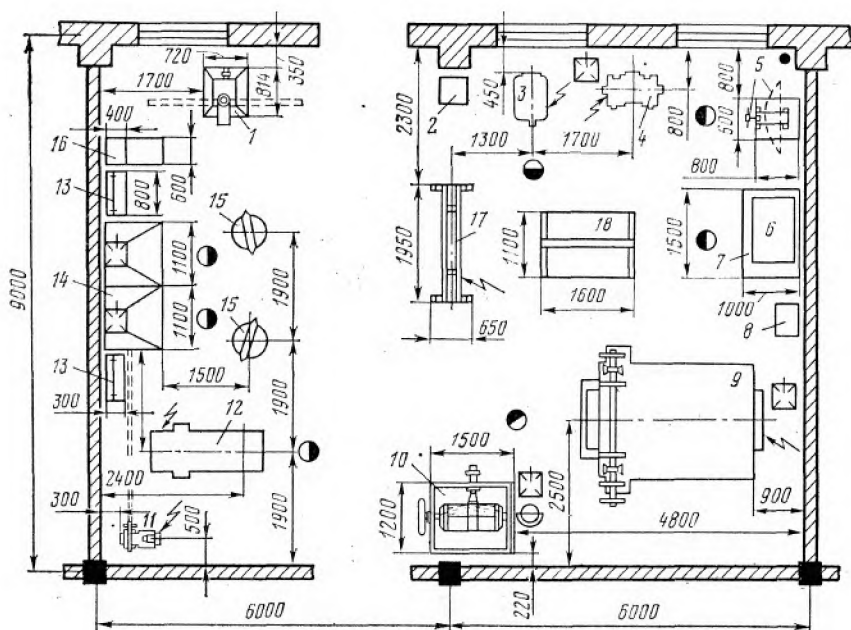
Кузнечное отделение ПАТ: 1 – стенд для рихтовки рессор; 2 – ящик для песка; 3 – вертикально-сверлильный станок; 4 – обдирочно-шлифовальный станок; 5 – стенд для сборки рессор; 6, 7 – правочная плита на подставке; 8 – щит для управления печью; 9 – камерная электрическая печь; 10 – установка для закалки рессорных листов; 11 – воздуходувка к горну; 12 – пневматический молот; 13 – ларь для кузнечного инструмента; 14 – кузнечный горн на два огня; 15 – наковальня; 16 – ящик для угля; 17 – стенд для испытания рессор; 18 – стеллаж для рессорных листов
